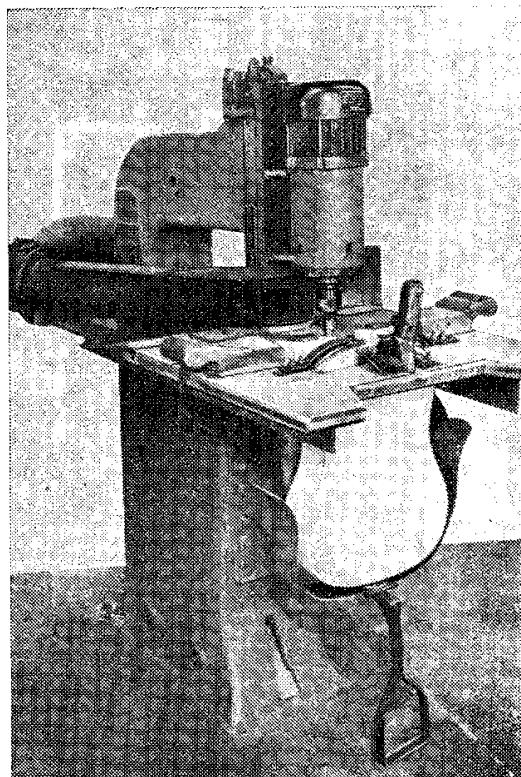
Фрезерование гнезда в корпусе гитары под пятку грифа на фрезерно-копировальном станке с дополнительным устройством
